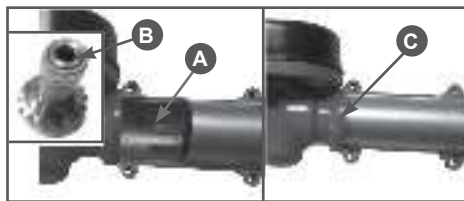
Совмещение вала штанги с отверстием вала редуктора
